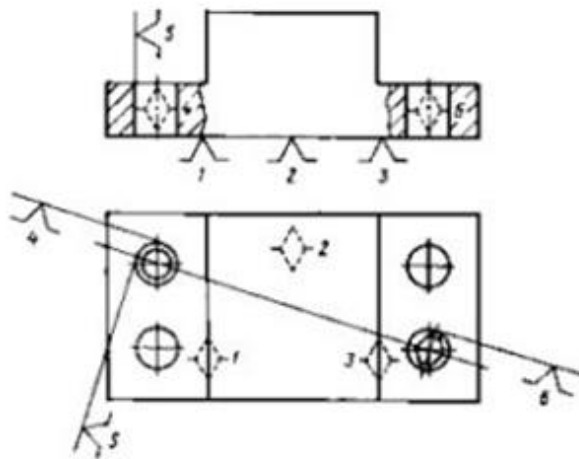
Схема базирования корпусной детали в конусах по главному отверстию, двойная направляющая (точки 1,2,3,4); опорные (точки 5,6).
